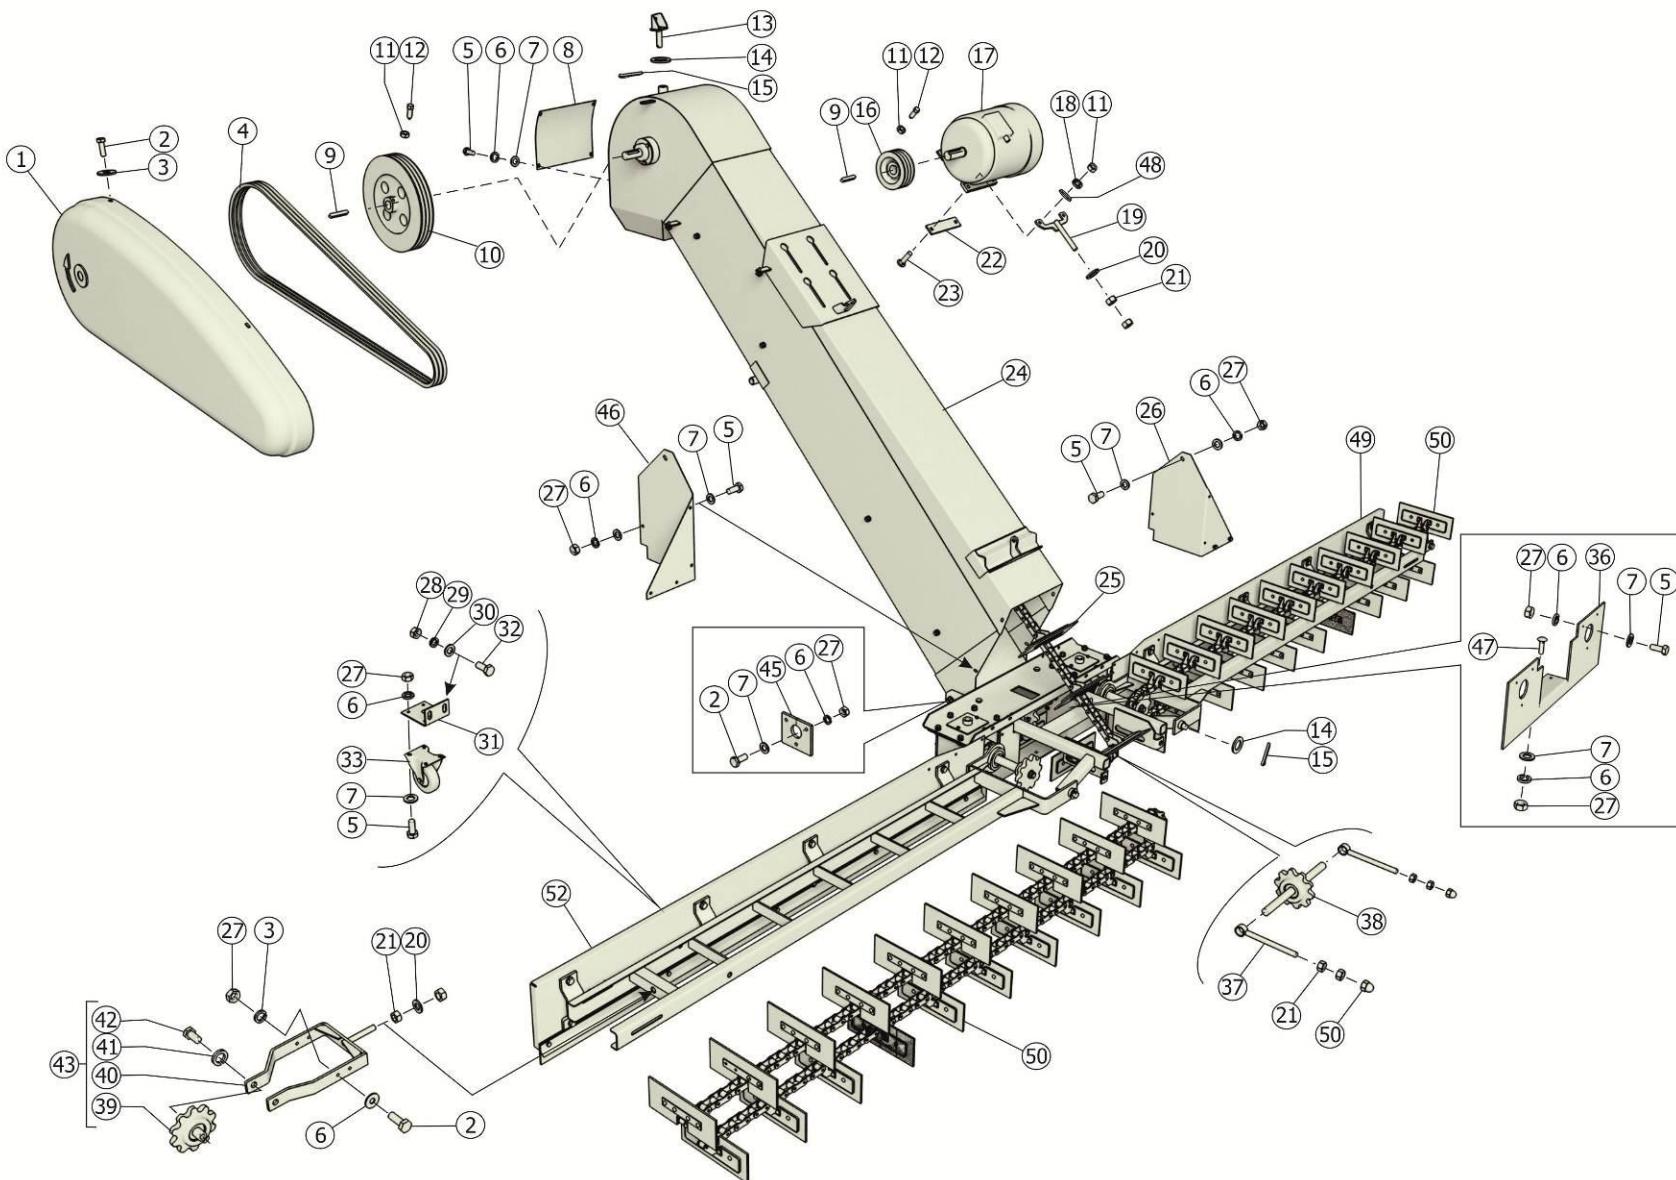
Транспортер загрузочный МЗС-90.23.000
